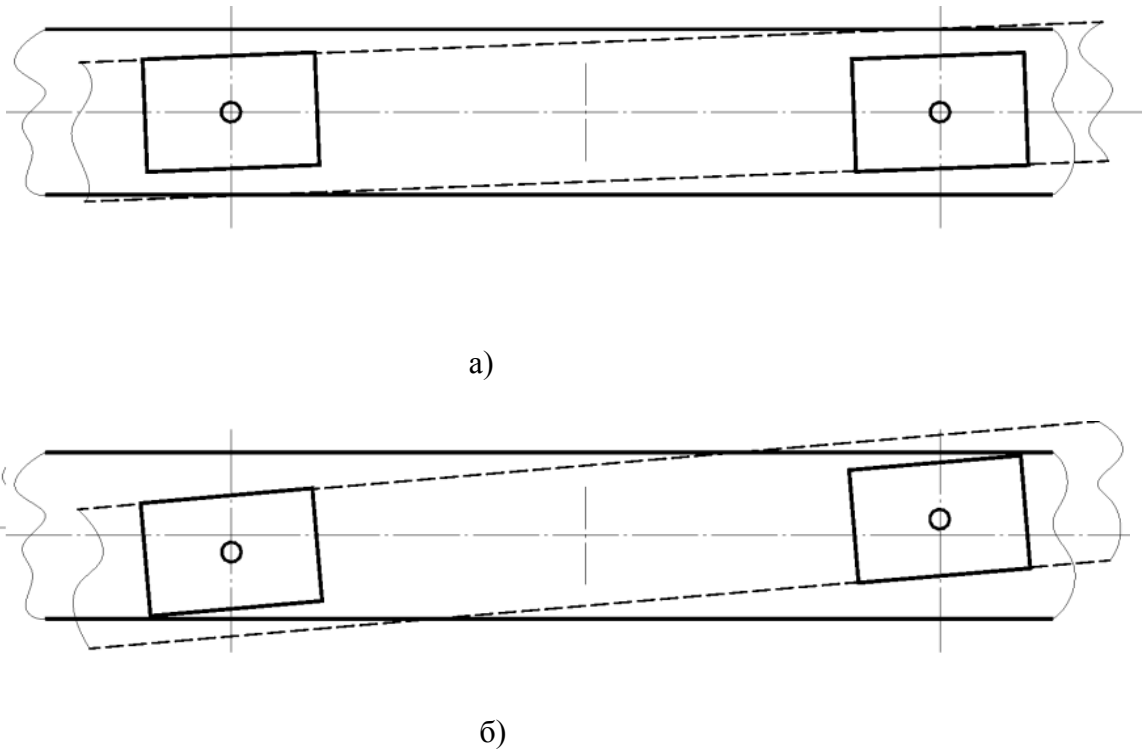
Фазы взаимодействия шпонок УТЗ и корпуса подшипника
